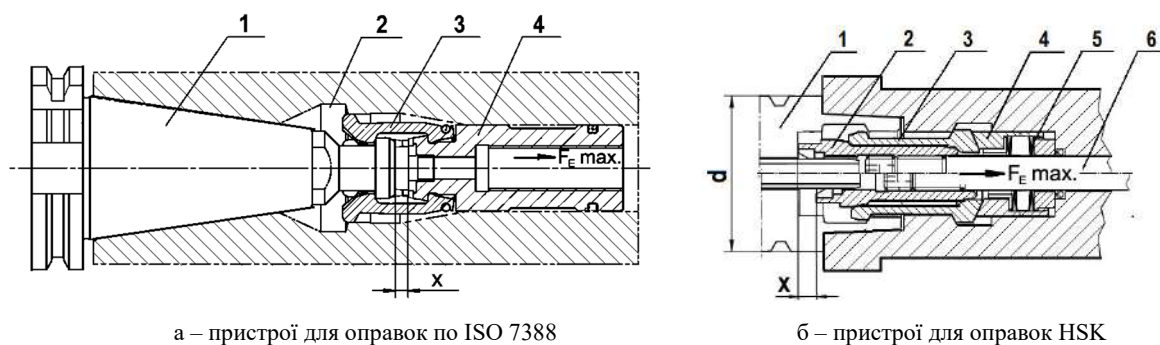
Захоплюючі пристрої для інструментальних оправок.
